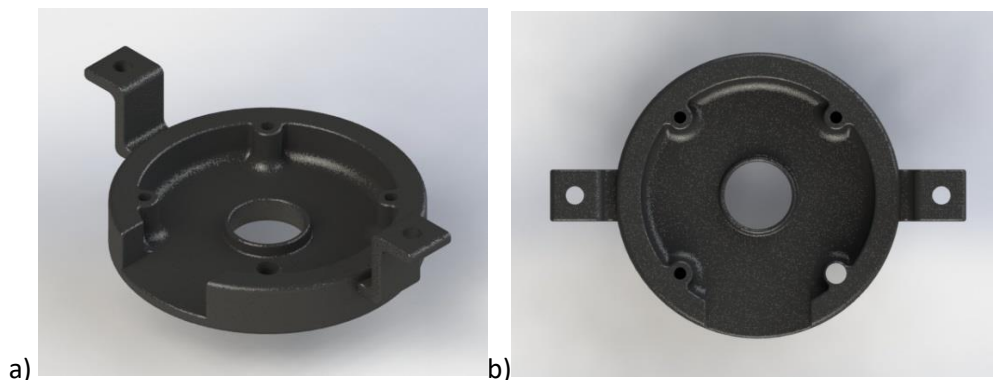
2º Modelo do suporte das placas a) vista cavaleira b) Vista de cima
